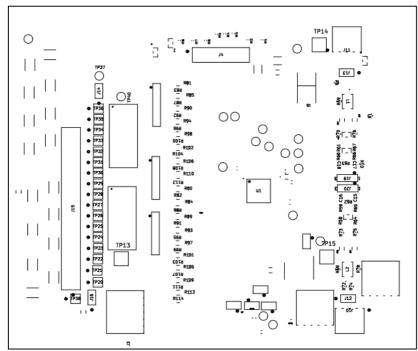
A BQ79616EVM Layout PCB 3D viewer
